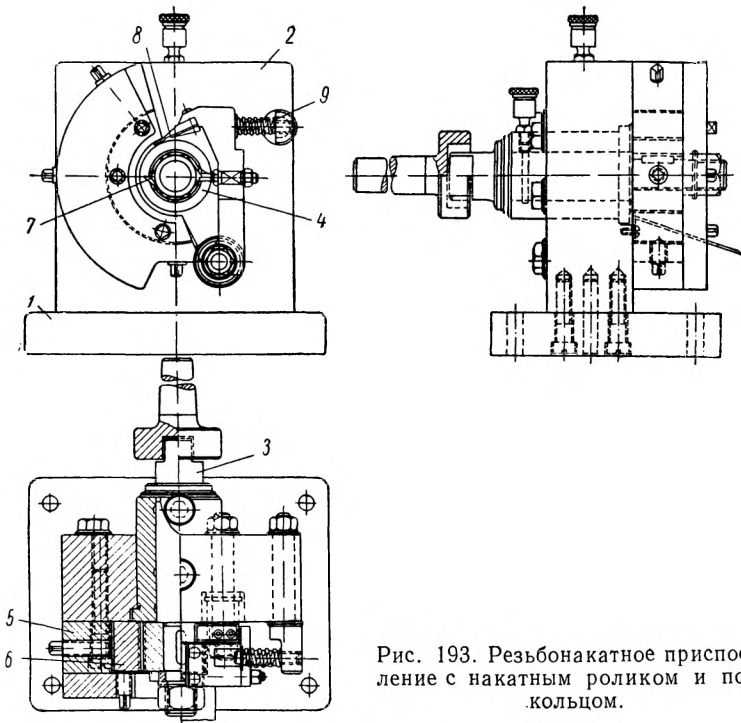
Резьбонакатное приспособление с накатным роликом и полукольцом.
